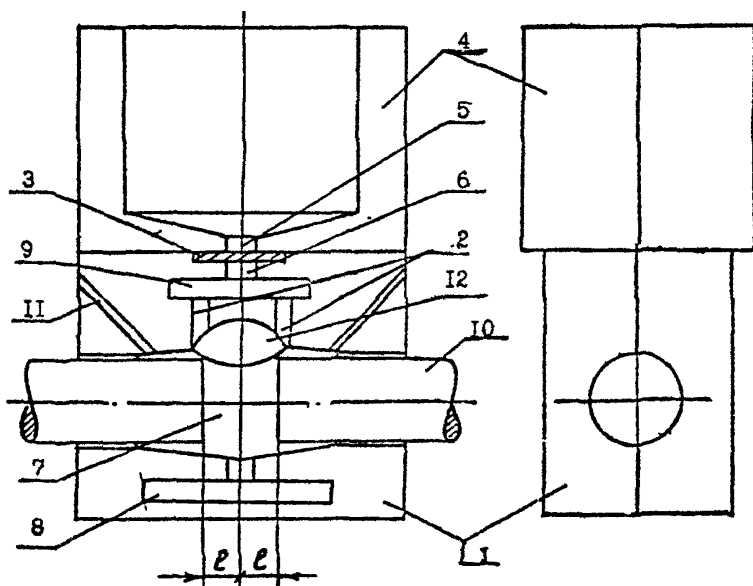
Сборка формы и тигля при сварке горизонтального соединения стержней
